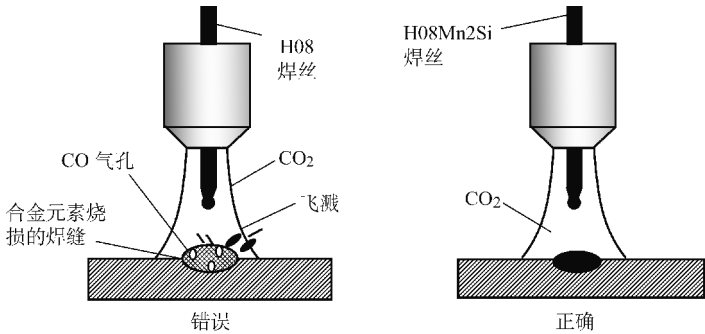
CO₂ 焊接工艺忌用普通焊丝
